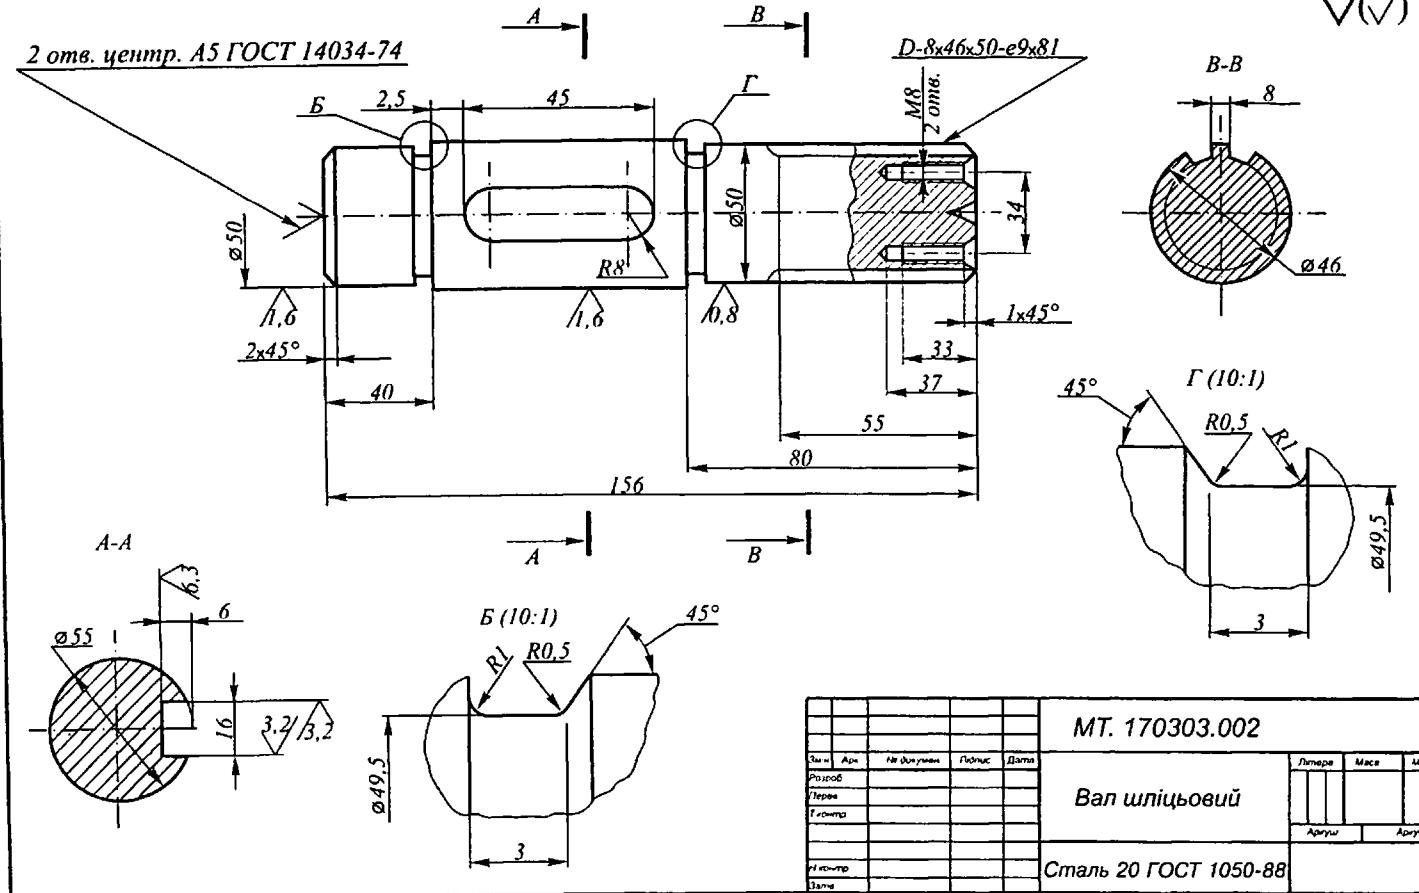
Приклад оформлення кресленника шліцьового вала
